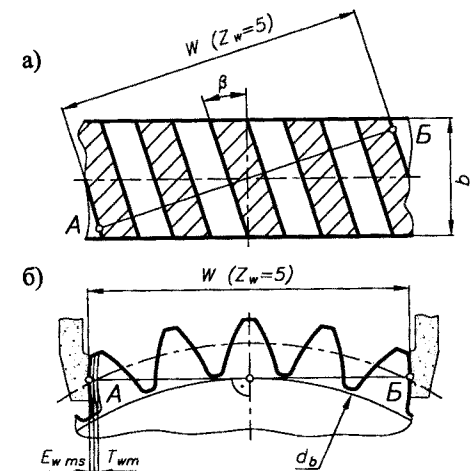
Схема замера длины общей нормали при числе охватываемых зубьев $Z_w = 5$ для цилиндрических колес:
